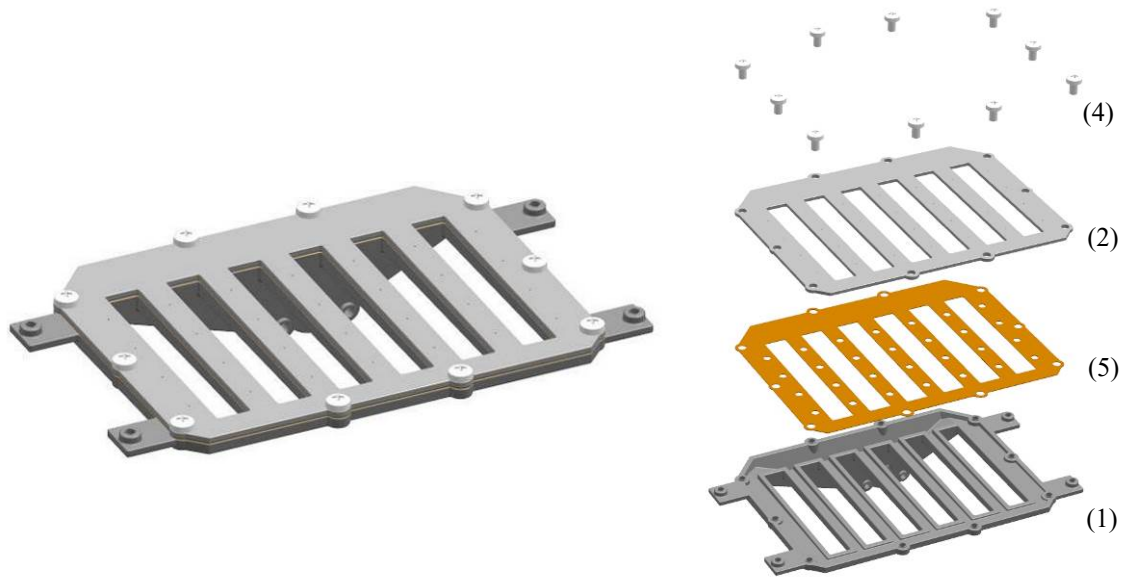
Corpo e tampa em chapa, versão 2 (conjunto montado e vista em corte)
